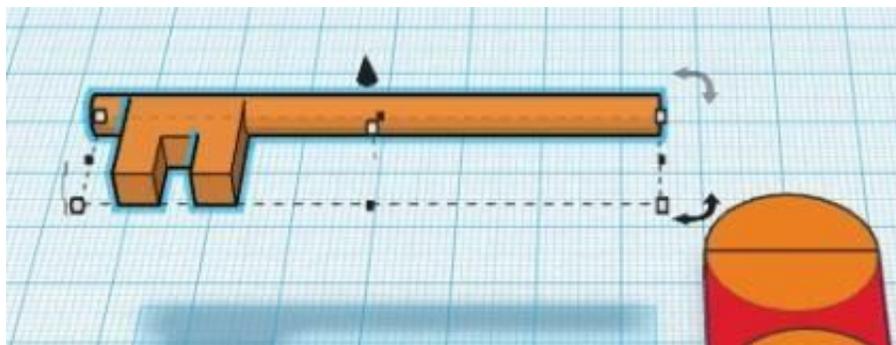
TIGE ET PANNETON PARALLÈLES AU PLAN DE CONSTRUCTION
